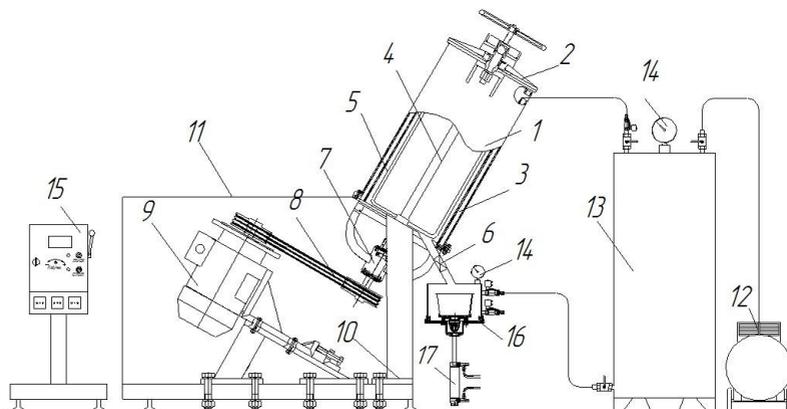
Промышленная машина для приготовления хлебопекарного теста механическим способом разрыхления
